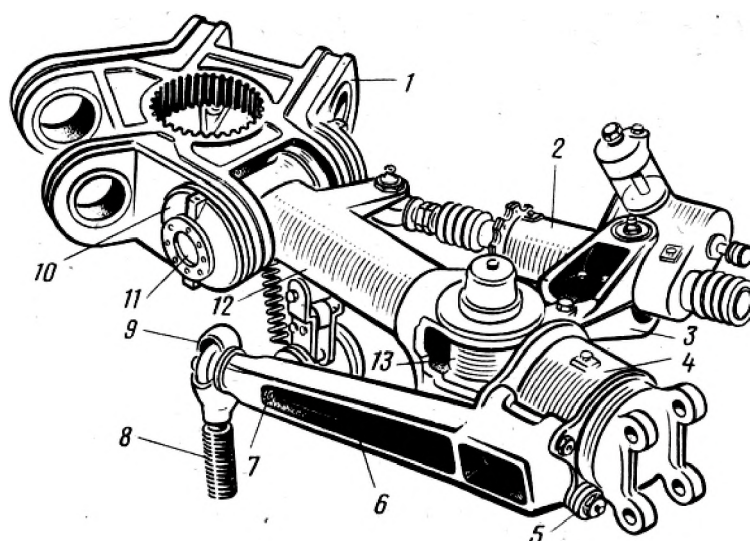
Втулка верхнего НВ вертолета Ка-26 [5]:
